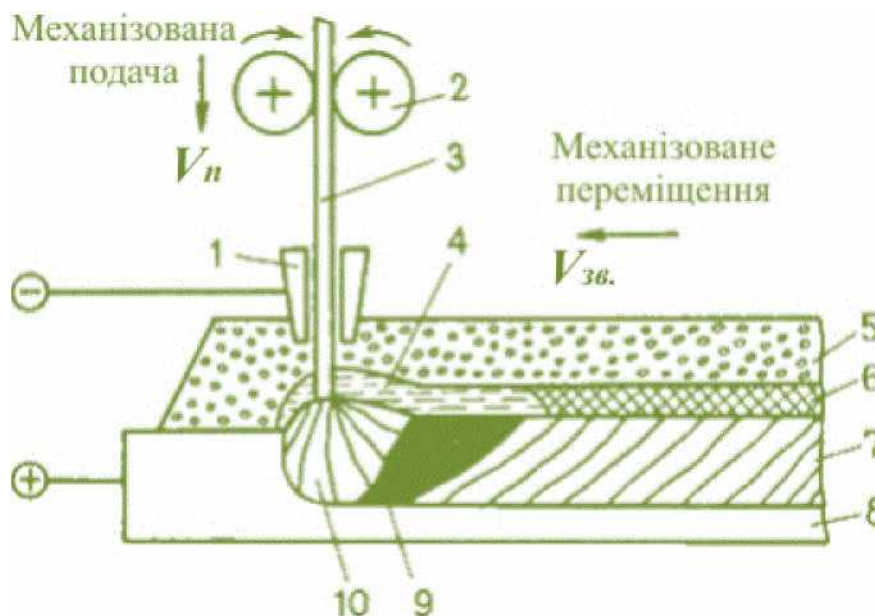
Схема автоматичного дугового зварювання під флюсом
